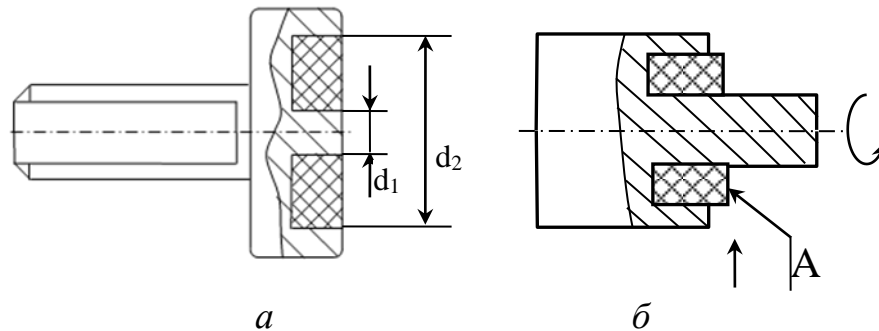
Золотник клапана із гумовим ущільненням (а) та заготовка для виготовлення золотника (б)
